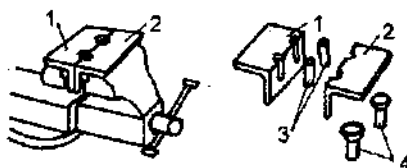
Приспособление для изготовления заклепок: 1, 2 — уголки с полуотверстиями; 3 — заготовки; 4 — заклепки
